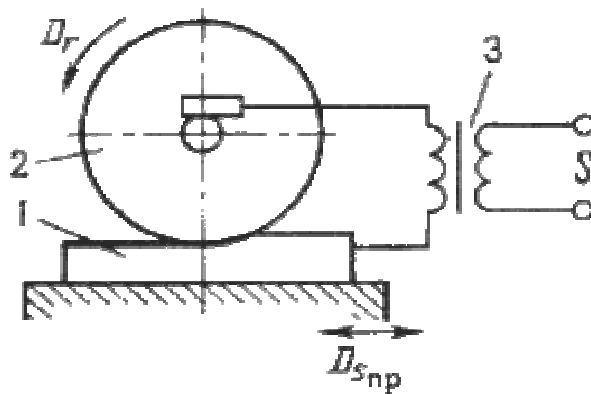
Схема электроконтактной обработки плоской поверхности: 1 – обрабатываемая заготовка; 2 – инструмент-электрод; 3 – трансформатор
